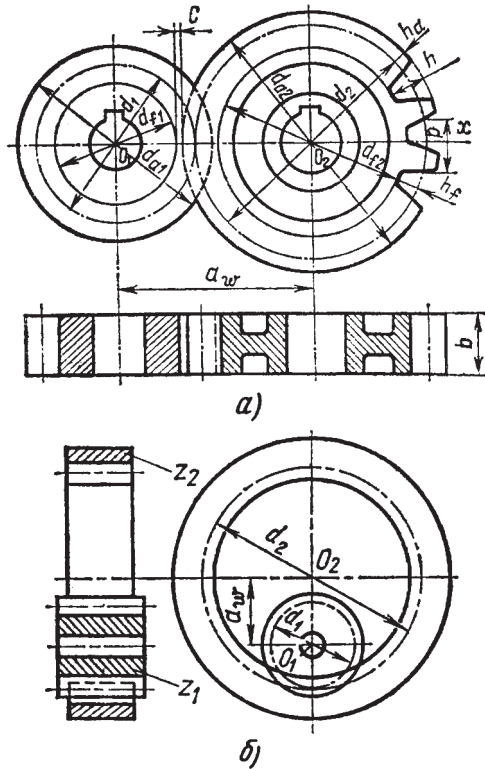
Цилиндрические прямозубые передачи и их основные размеры
